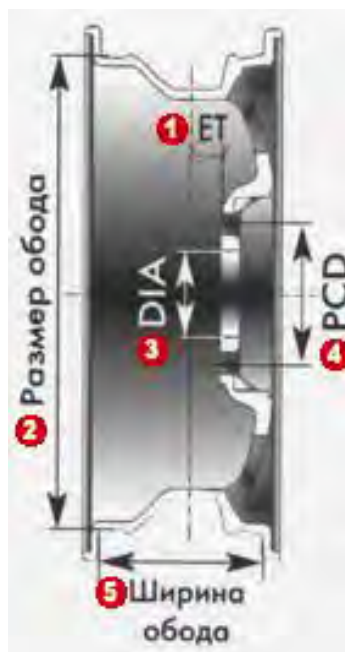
Обозначения размера колесного диска. Маркировка колеса (диска)
